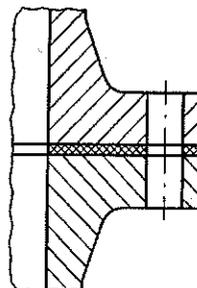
Vorschweißflansch mit durchgehender Dichtung
